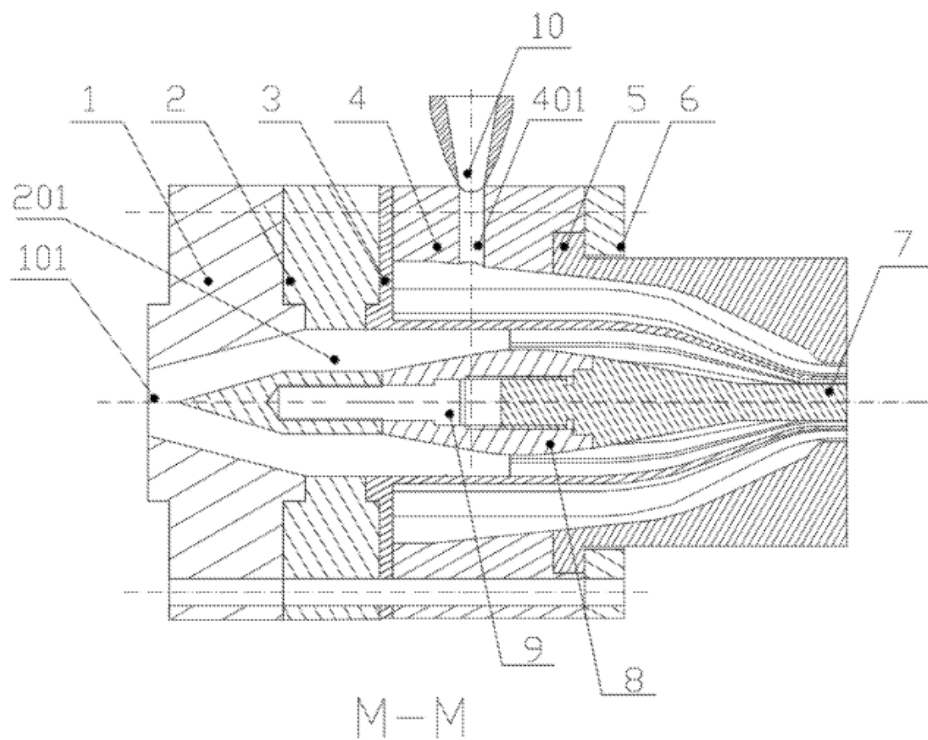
Поздовжній розріз форми (М-М)
